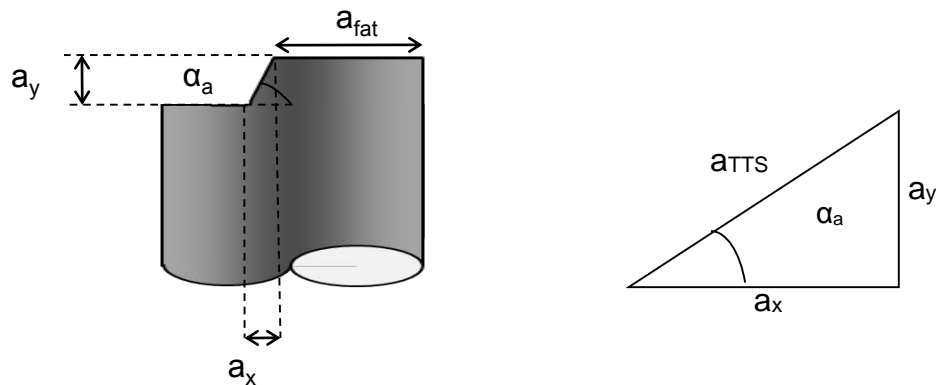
Esquema donde se muestran las proyecciones horizontal y vertical de la fisura generada por la acción del ambiente agresivo.
